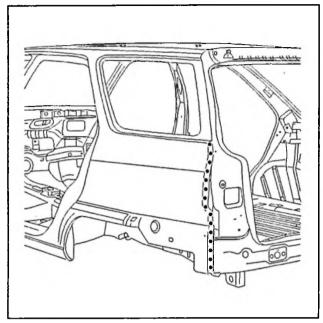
CP08MC Souder par points "bouchon" MAG. Meuler les points de soudure MAG.
